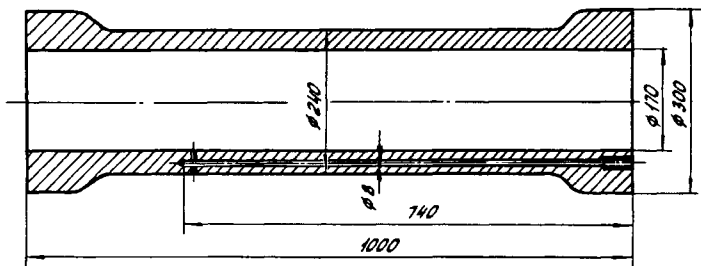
Пример нетехнологичной конструкции корпуса гидравлического цилиндра
